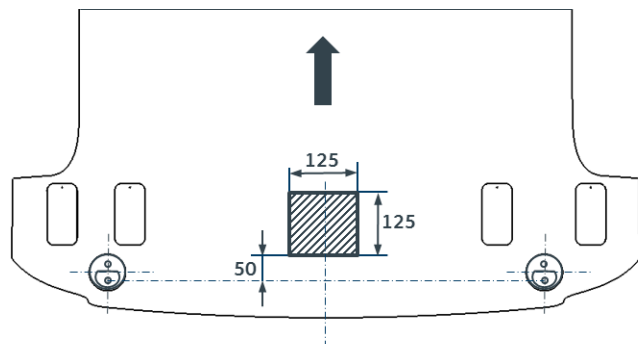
posizione e apertura per la bocchetta a pavimento sulla parte posteriore della vettura (quote in mm)
